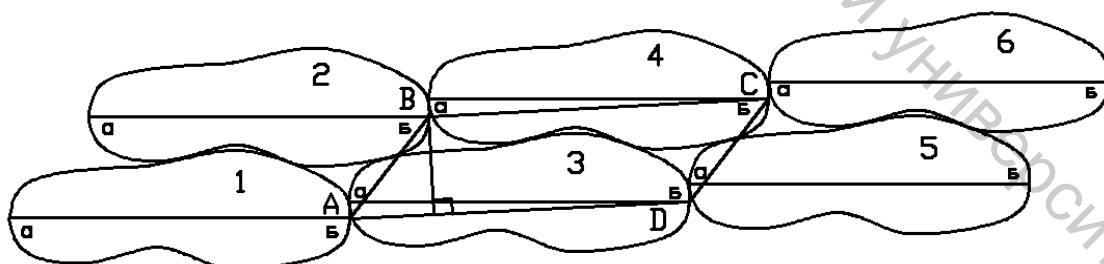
Схема совмещения подошв и стелек в одну сторону (вариант 3)
